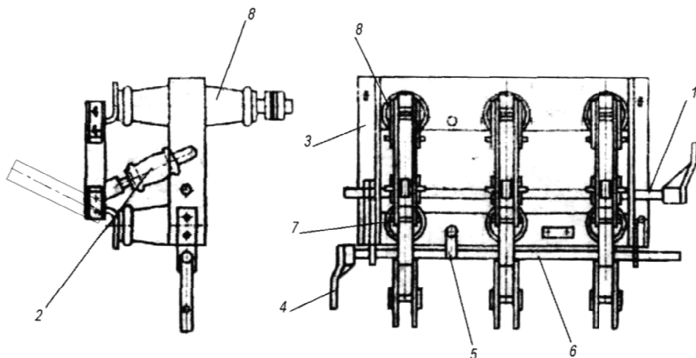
Трёхполюсный разъединитель внутренней установки типа РВФЗ-6-10:
